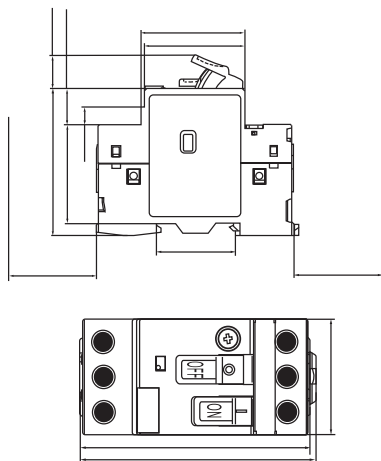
DIMENSÃO TOTAL E DIMENSÃO DE INSTALAÇÃO DE TRS2-25
